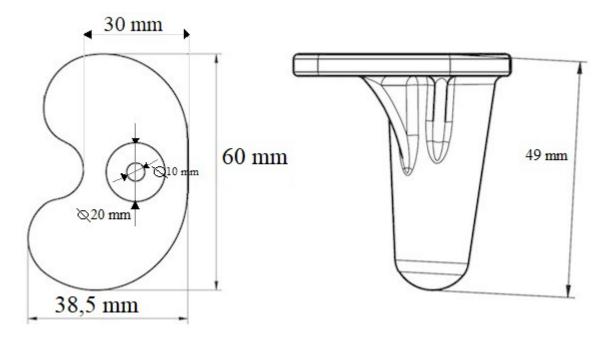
Budowa endoprotezy stawu kolanowego [8.2]
